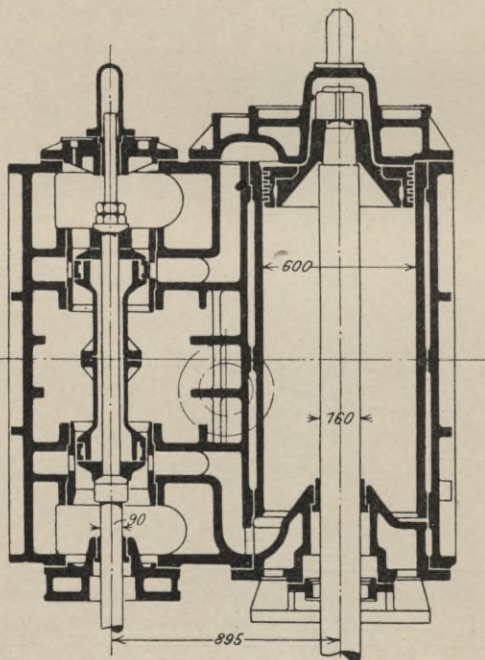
Hochdruckzylinder des Passagierdampfers „Gneisenau“.
